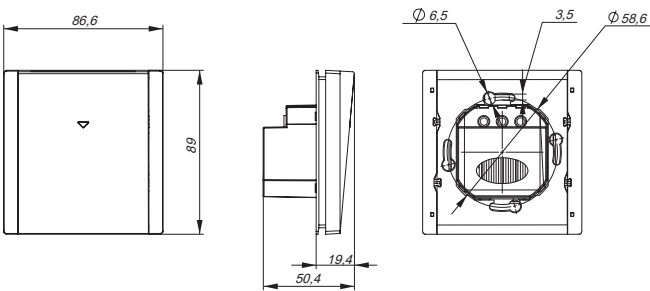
Габаритные и установочные размеры выключателя / Figure 2 – Overall and installation dimensions of the switch / 2 сурет – Ажыратқыштың габариттік және орнату өлшемдері / Figura 2 – Dimensiunile generale și de instalare ale întrerupătorului / 2-rasm – Viklyuchatelning gabaritlari bo’yicha va o’rnatilish natijasidagi o’lchamlari
